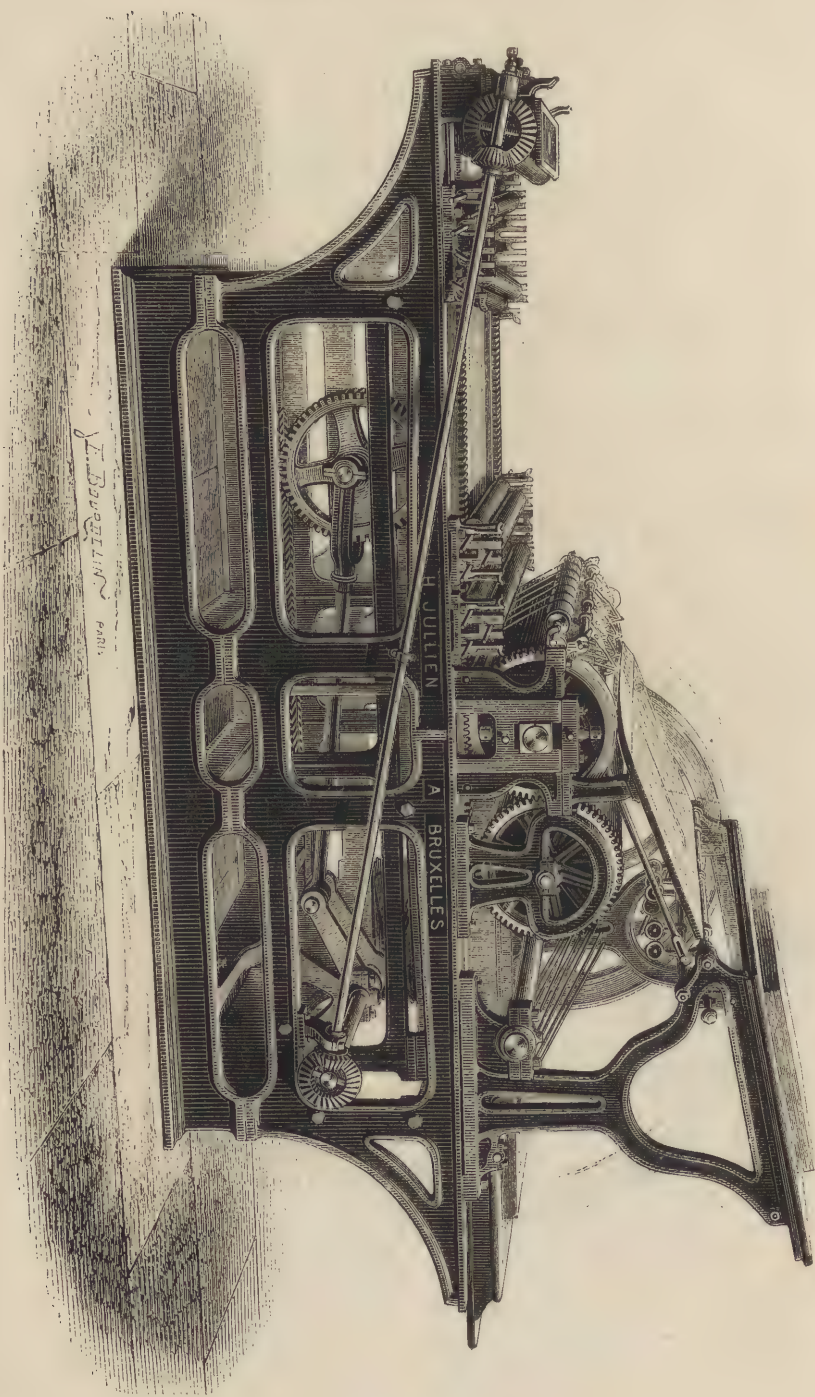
MACHINE EN BLANC. A MARCHÉ RAPIDE.
